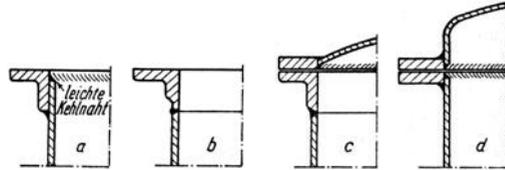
Schweißnähte an Winkelringen.
